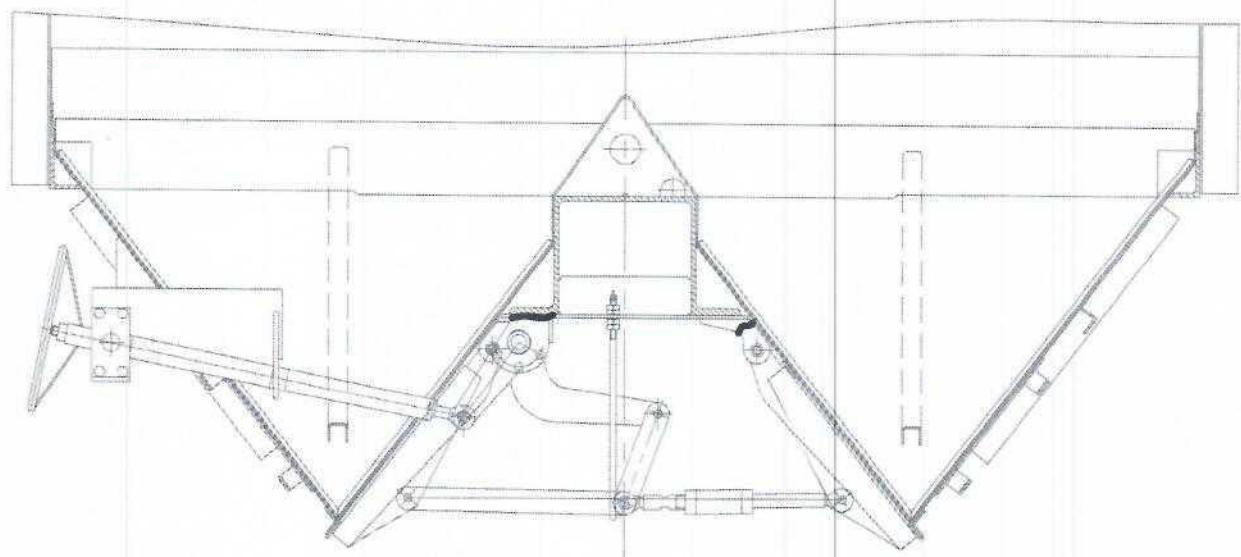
Трешины крепления крышки разгрузочного люка
